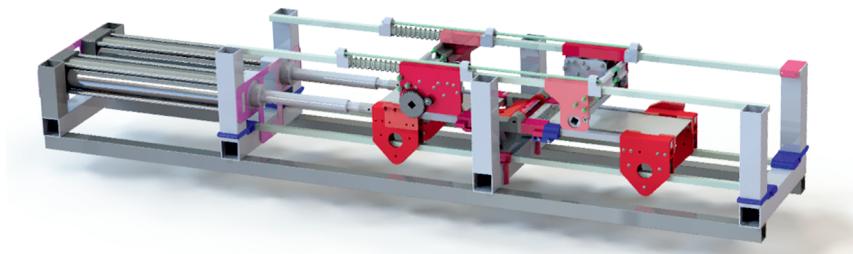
3D-модель стенда для изготовления древесного волокна
